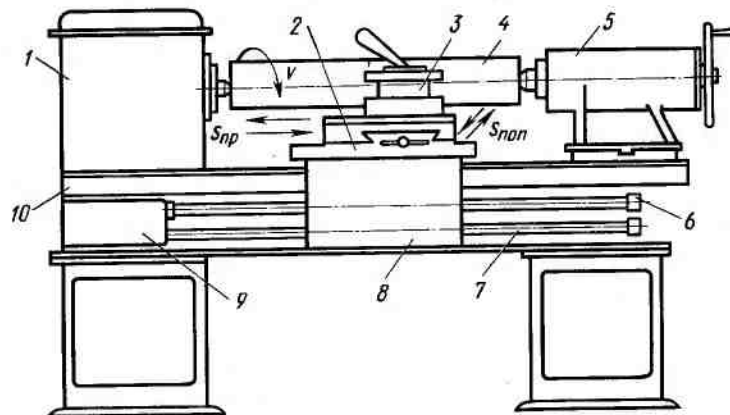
Основные узлы и движения токарно-винторезного станка: 1 — передняя бабка, 2 — суппортная группа, 3 — резцедержатель, 4 — обрабатываемая заготовка, 5 — задняя бабка, 6 — ходовой винт, 7 — ходовой вал, 8 — фартук, 9 — коробка подач, 10 — станина
